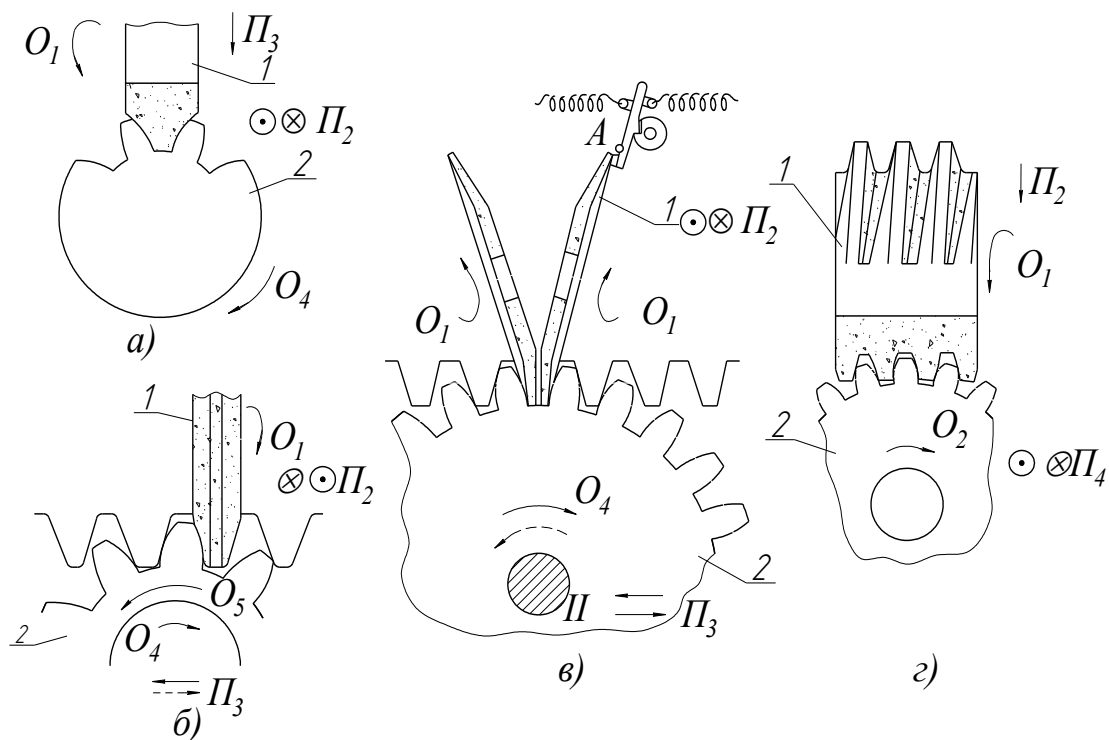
Способи шліфування циліндричних зубчастих коліс: 1 – круг; 2 – колесо.
